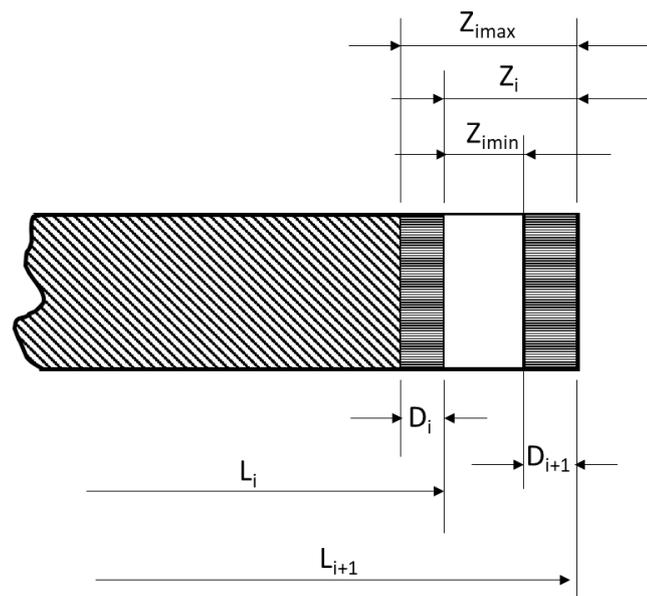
Superfície que será usinada mostrando dimensões e sobremetal parcial com respectivas tolerâncias.
